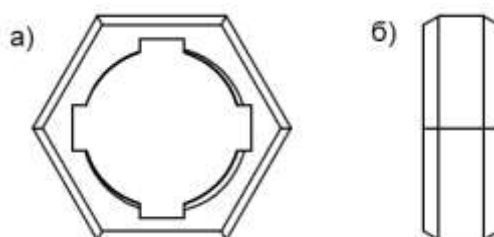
Гайка M22x1,5-6g: а) – вид спереди; б) – вид сбоку
